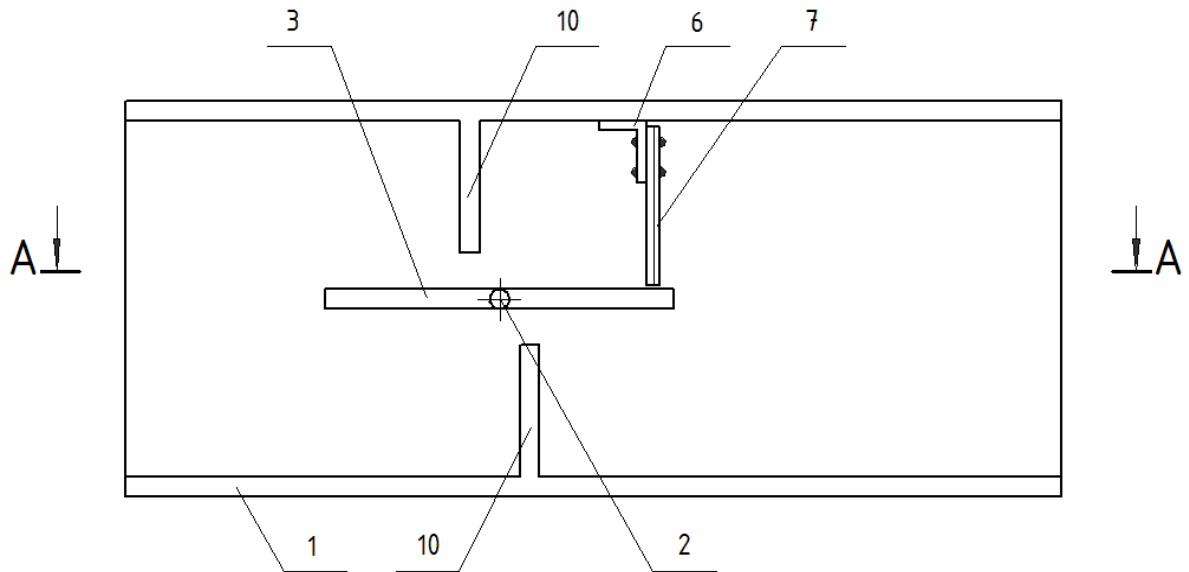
Схема устройства: продольный разрез огнезадерживающего клапана
